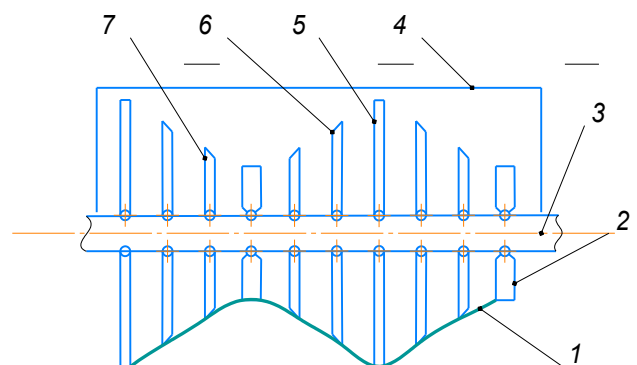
Фрагмент схеми ножів ротора удосконаленої фрези: 1 – профіль гребня; 2 – ніж КПП-1,5; 3 – вал ротора фрези; 4 – захисний кожух; 5 – прямий ніж; 6 – ніж із правим скосом; 7 – ніж із лівим скосом
